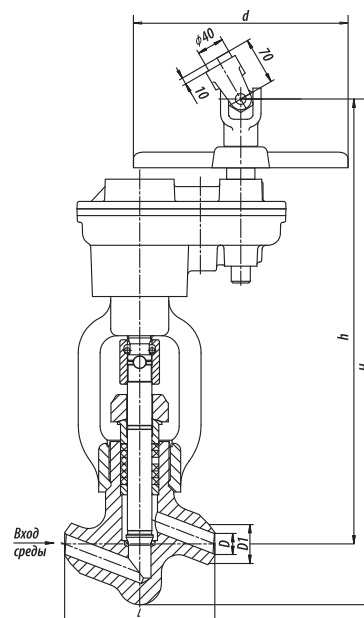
Клапан запорный DN32-65 с цилиндрическим редуктором
